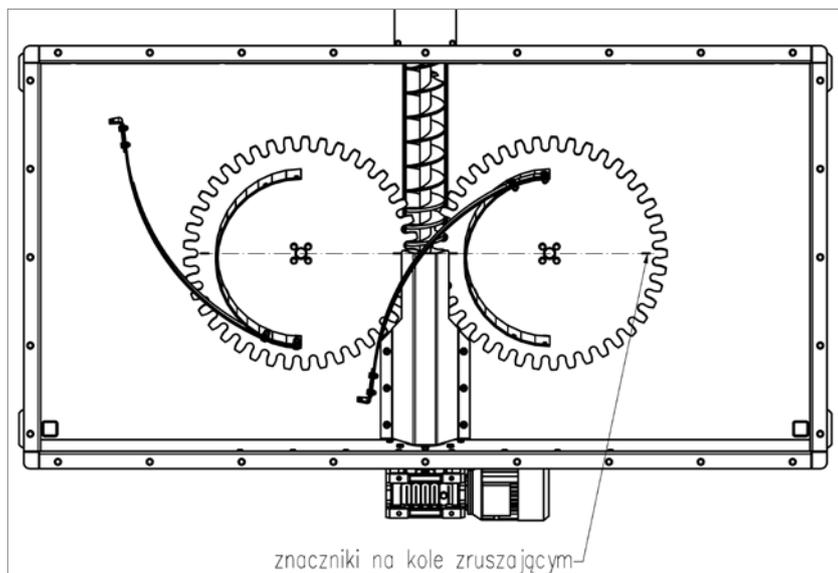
Схема установления смешивающих колес в резервуаре, мощность до 120кВ
